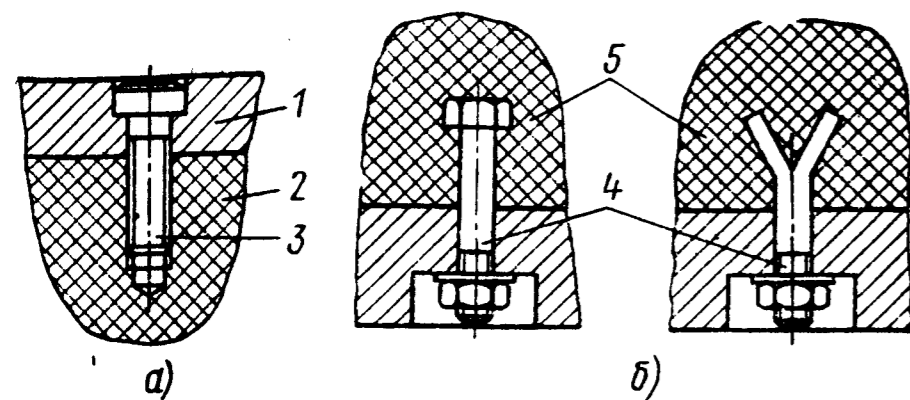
Способы крепления пластмассы к металлическим деталям штампа
